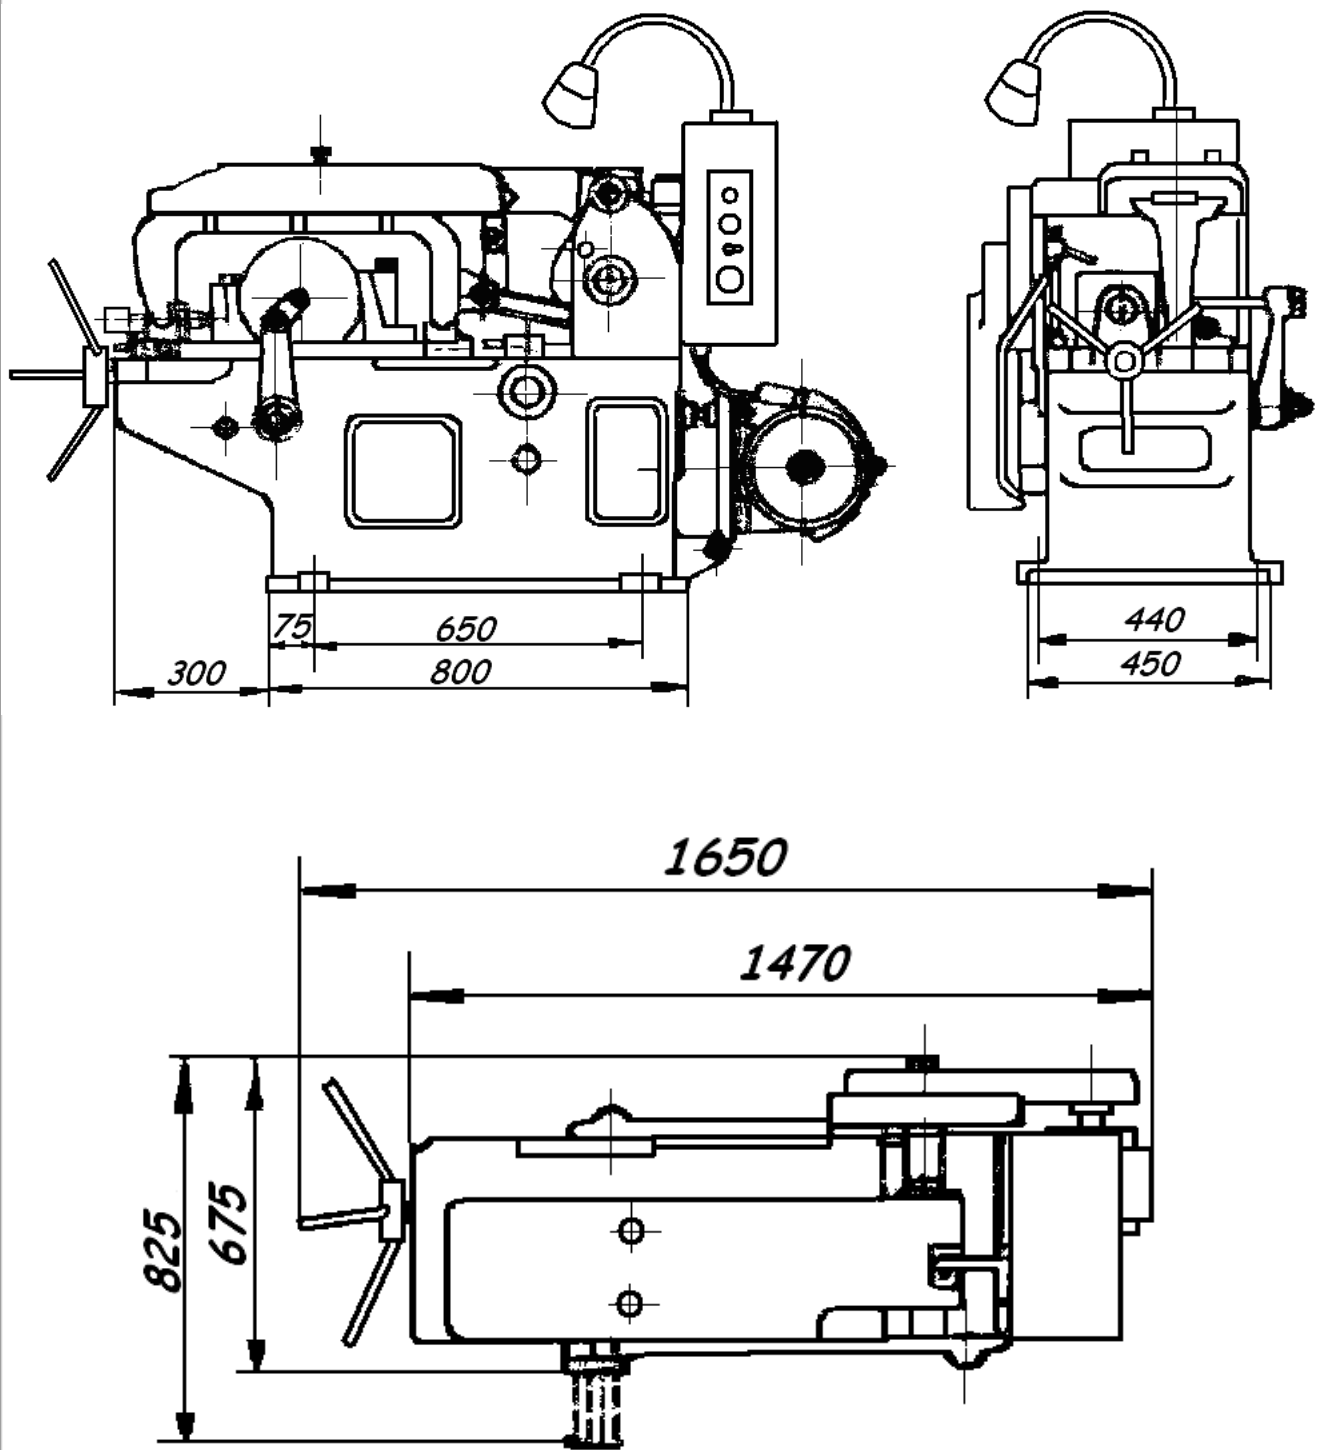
Общий вид станка с габаритными и установочными размерами.
